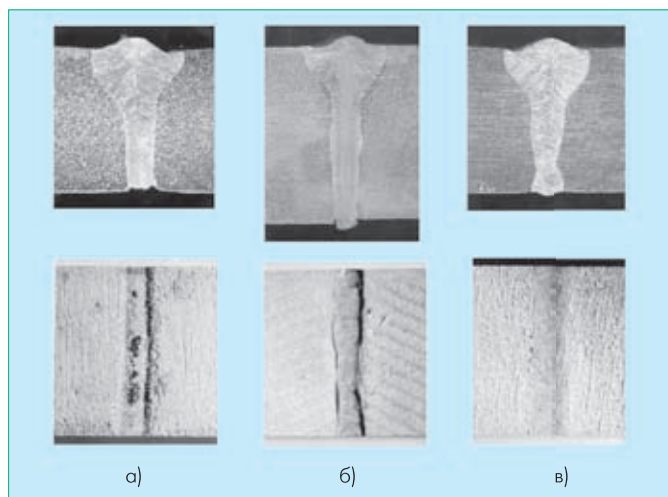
Макрошлифы и внешний вид поверхности обратного валика сварных швов, выполненных а) без его защиты, б) с защитой гелием и в) аргоном. Сталь марки 08X18H10Т толщиной 10 мм (а,б) и 12 мм. Сварка выполнялась по технологии [11,19]
